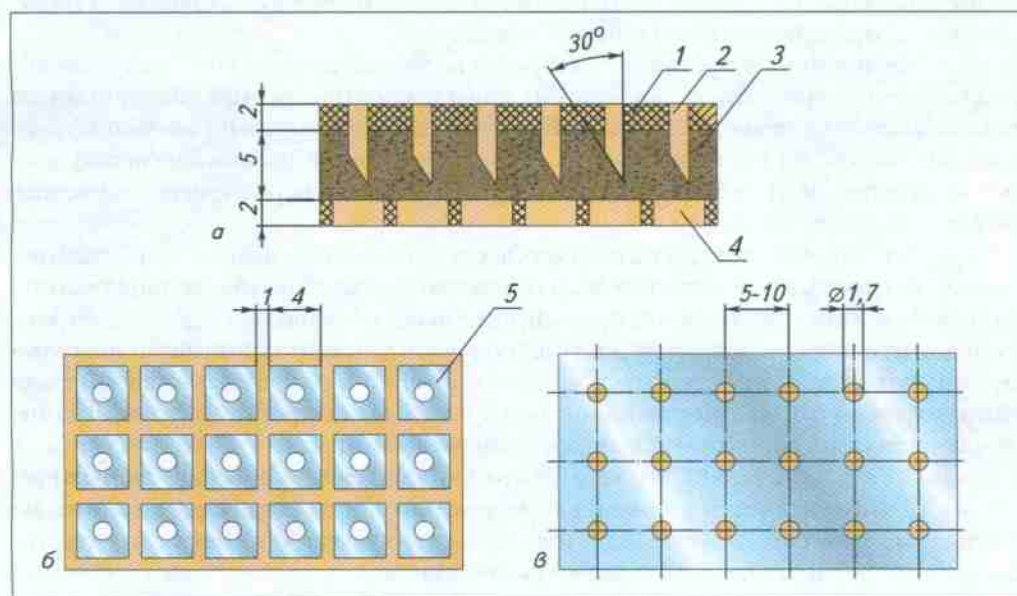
Устройство монтажной панели радиоконструктора: а — монтажная панель в сборе; б — вид сверху; в — вид снизу
